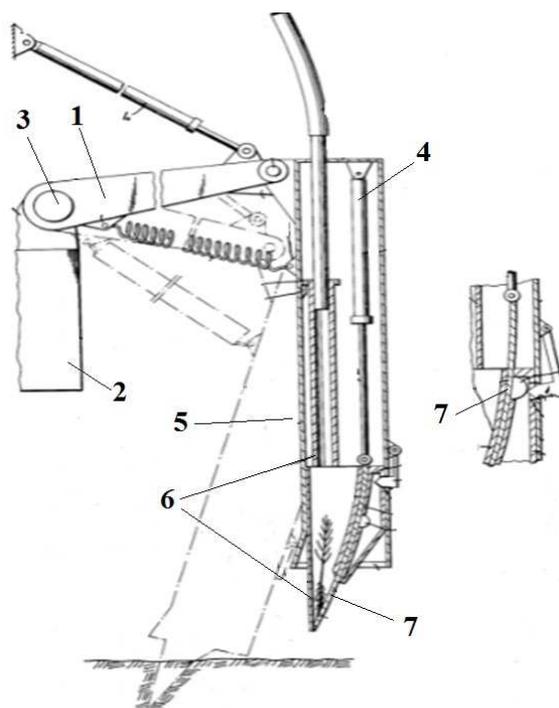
Схема копательно-посадочной машины по патенту 4067268 [13]:
